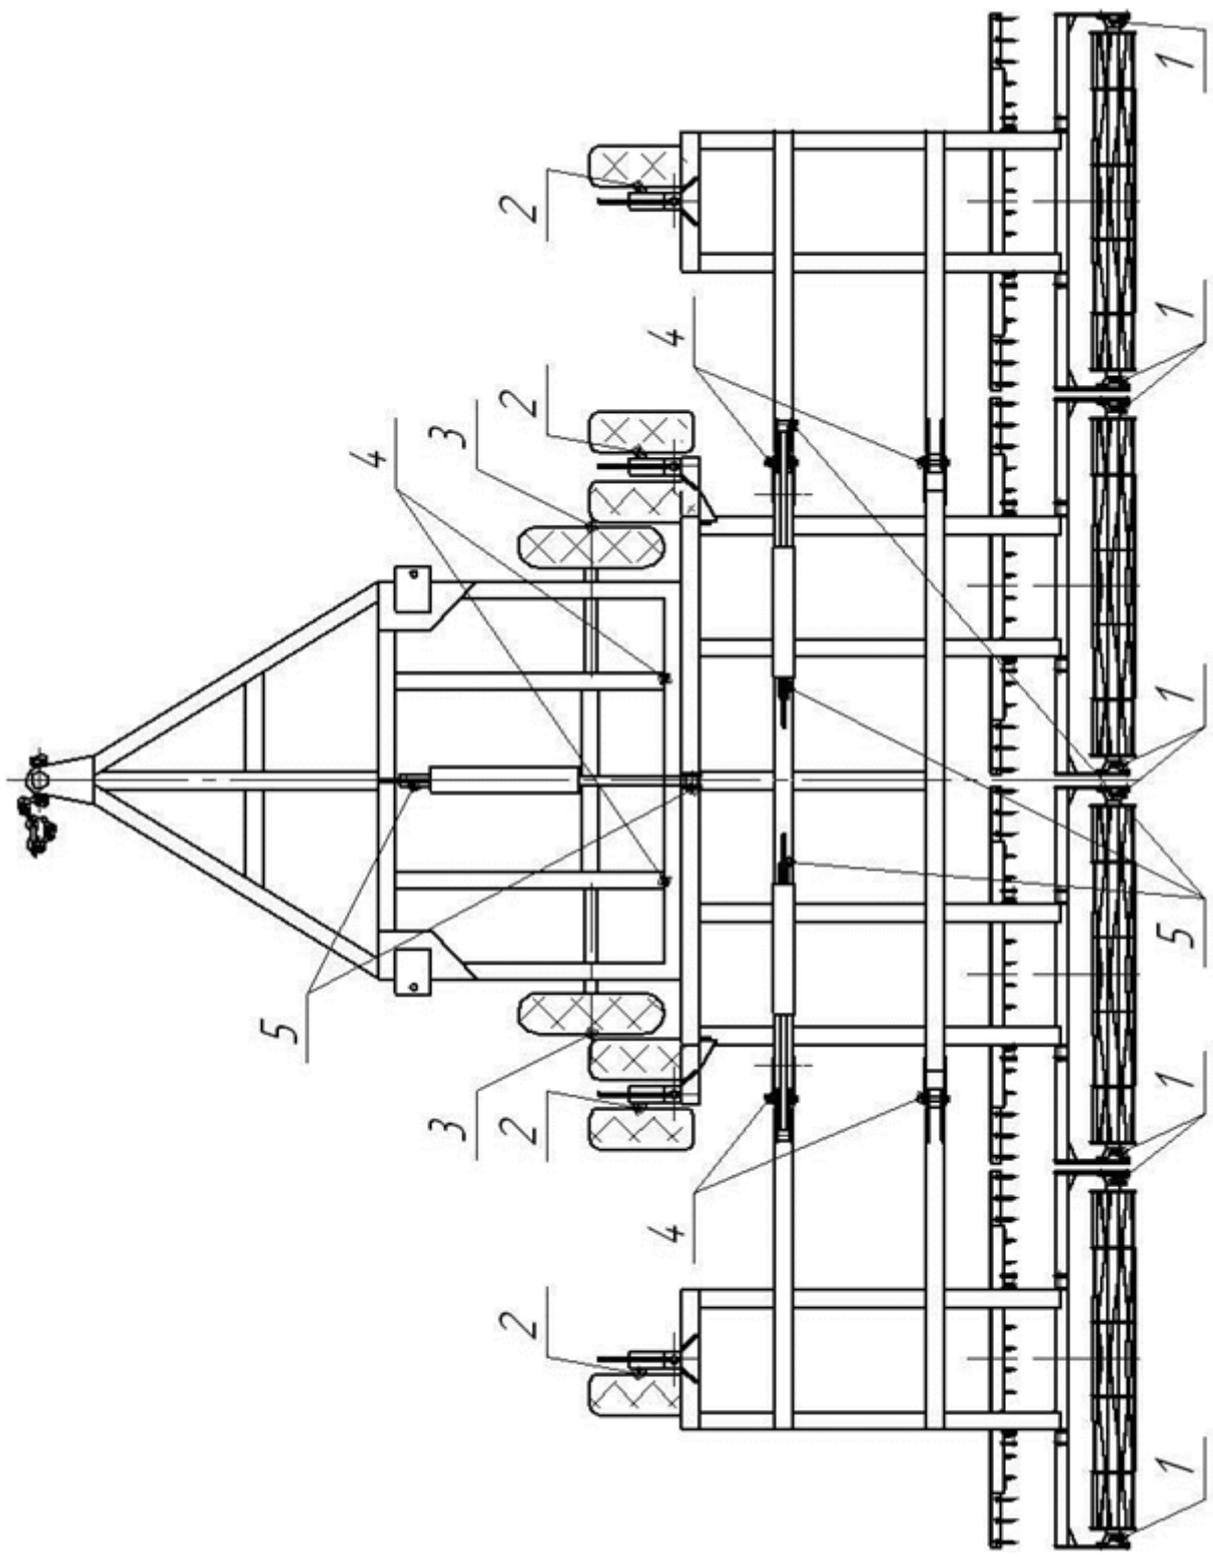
Карта смазки культиватора КБМ-7,2 КБМ-6, КБМ-8,0
